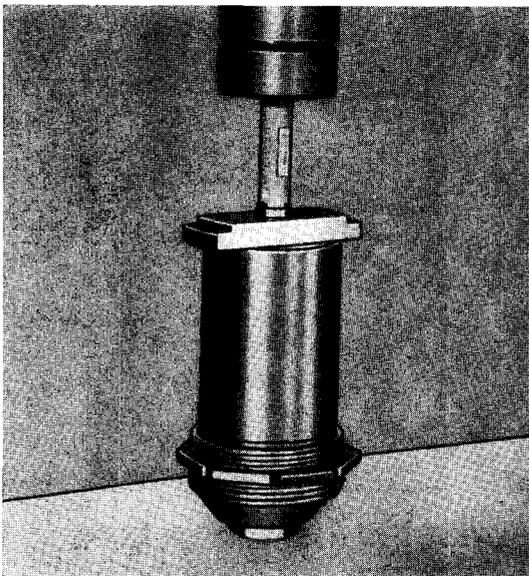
Kugellagerring in Lagerstellkappe eindrücken
